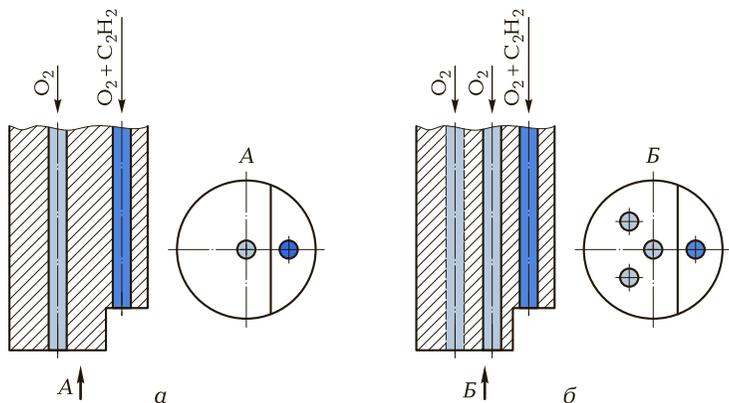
Схемы мундштуков для резки металла малой толщины:
